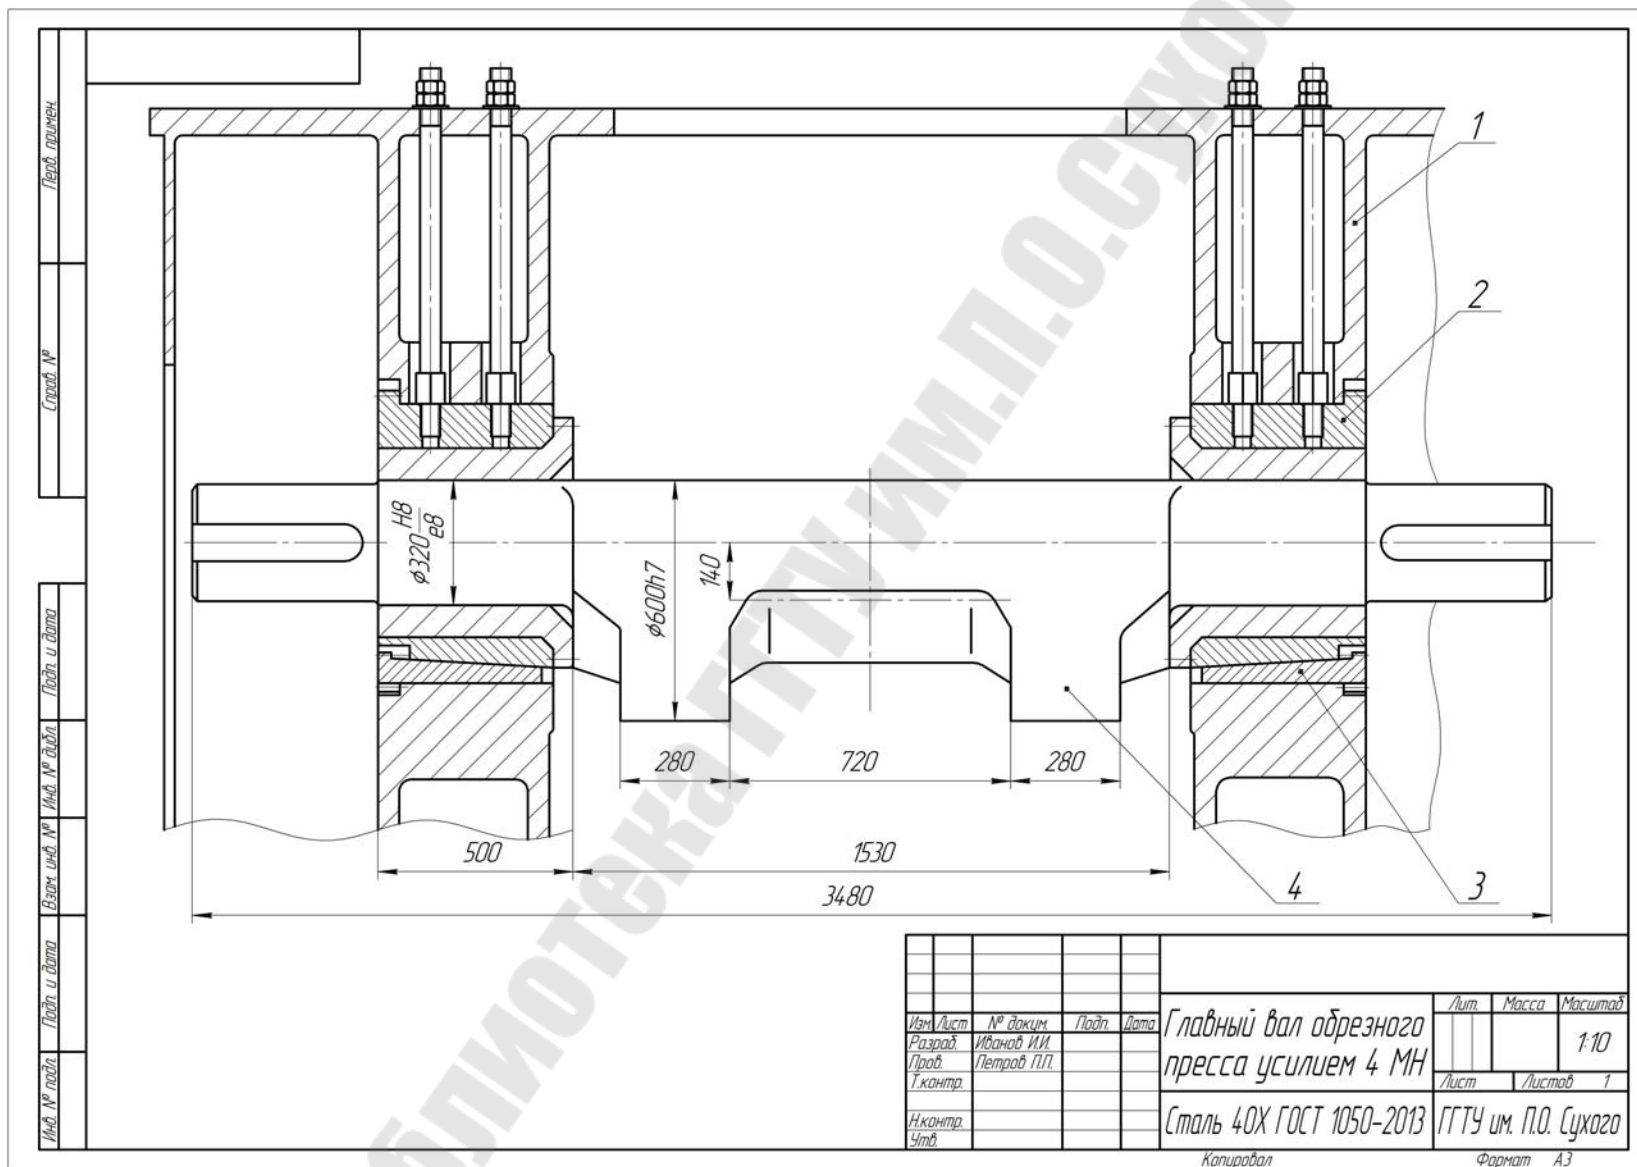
Главный вал в сборе обрезающего пресса усилием 4 МН
